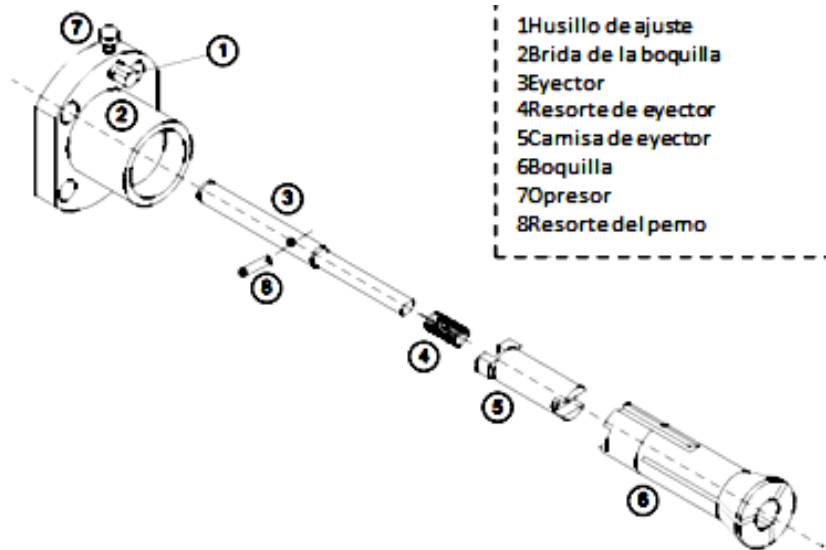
Vista explosiva de partes componentes del herramienta para cambio de boquillas máquina.
